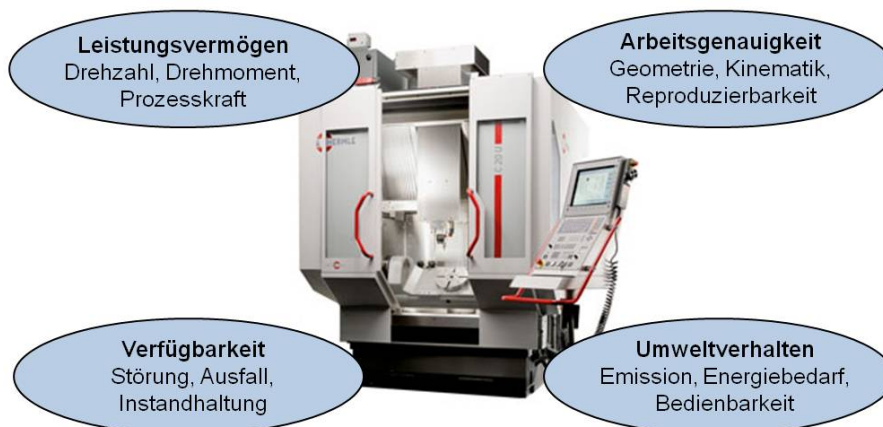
Eigenschaften von Werkzeugmaschinen [5]
